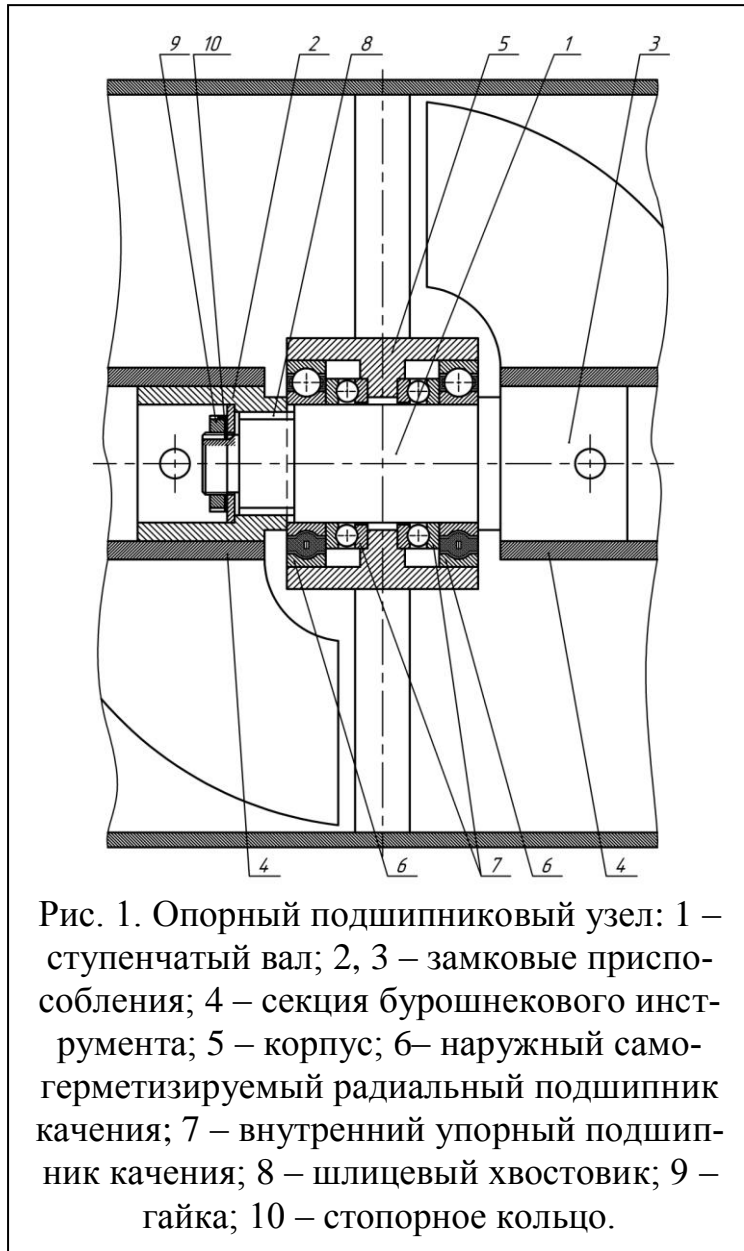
Опорный подшипниковый узел: 1 – ступенчатый вал; 2, 3 – замковые приспособления; 4 – секция бурошнекового инструмента; 5 – корпус; 6 – наружный самогерметизируемый радиальный подшипник качения; 7 – внутренний упорный подшипник качения; 8 – шлицевый хвостовик; 9 – гайка; 10 – стопорное кольцо.
